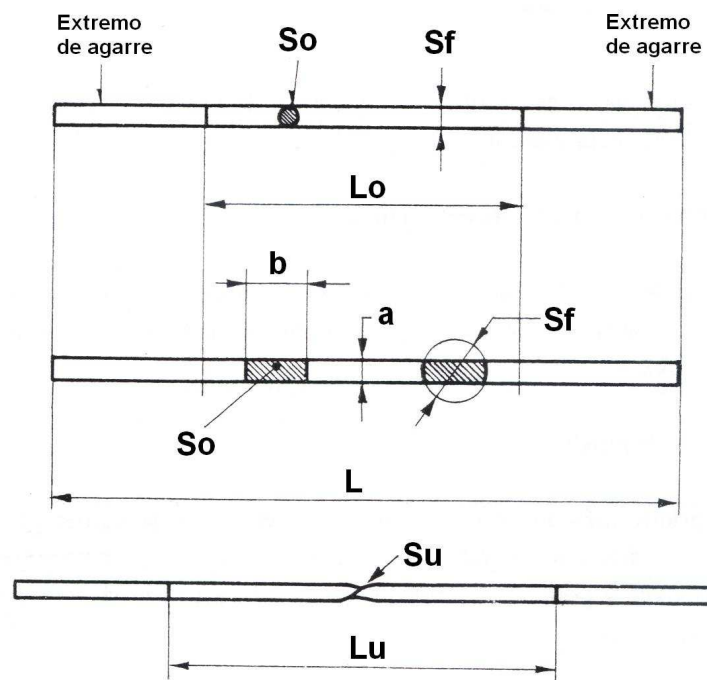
Probeta de alambre de acero para ensayo de tracción
